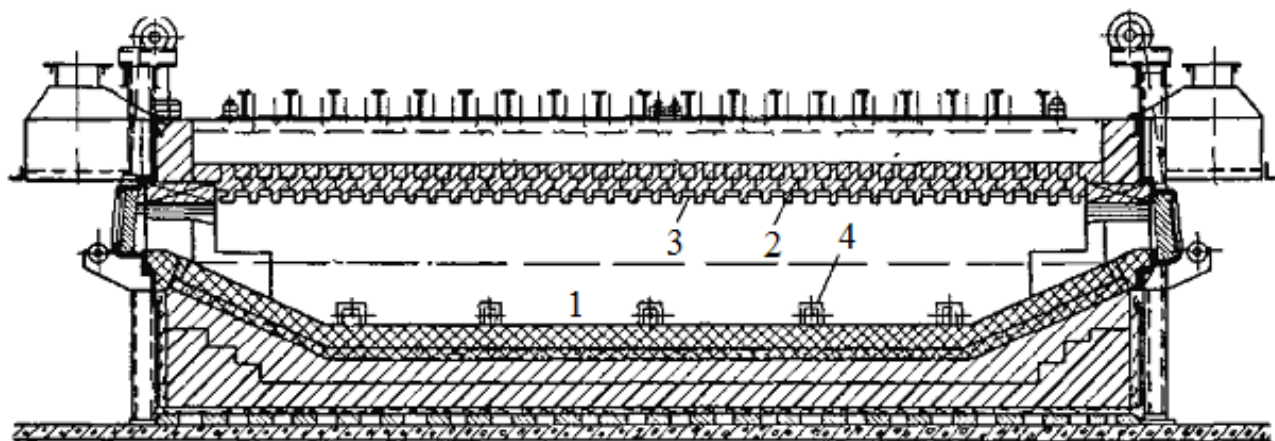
Электрический миксер: 1 – ванна; 2 – подвесной свод; 3 – нагреватели; 4 – лётки для выдачи металла
